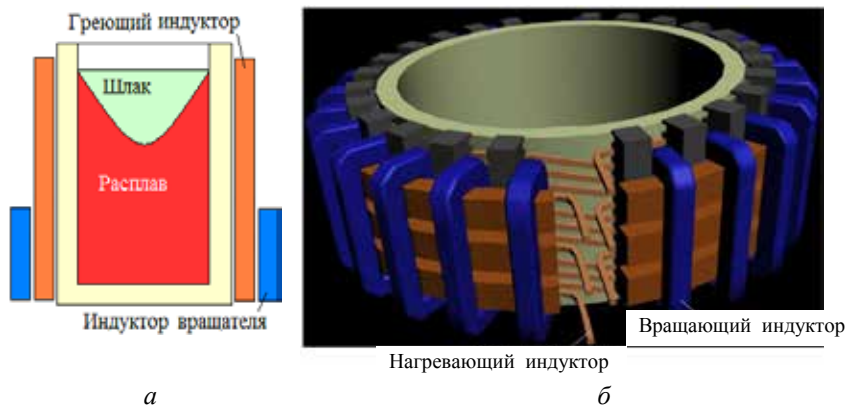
МПА с совмещением магнитопроводов нагревающего индуктора и индуктора вращателя:
